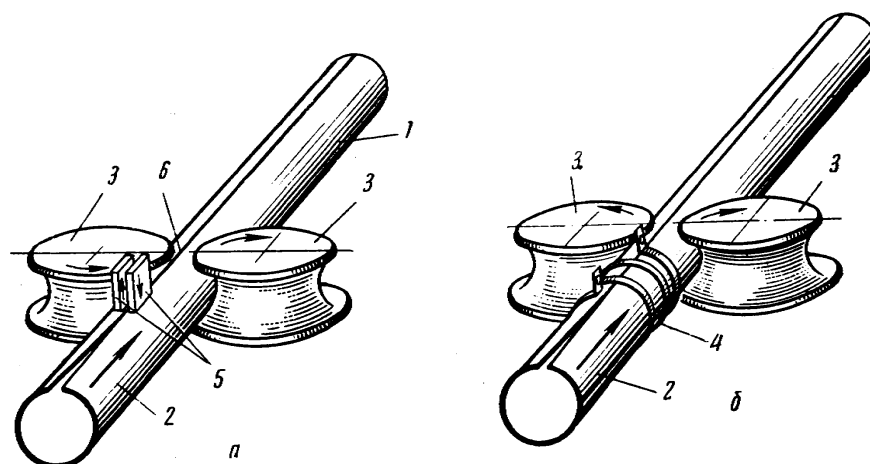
Схема сварки прямошовных труб контактным способом (а) и с помощью охватывающего кольцевого индуктора (б)
